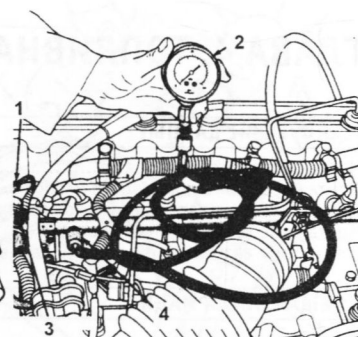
Чтобы проверить давление в топливной СВМ, Вам понадобится присоединить топливный манометр со шкалой 0-4.2 атм к патрубку проверки давления на топливной магистрали
